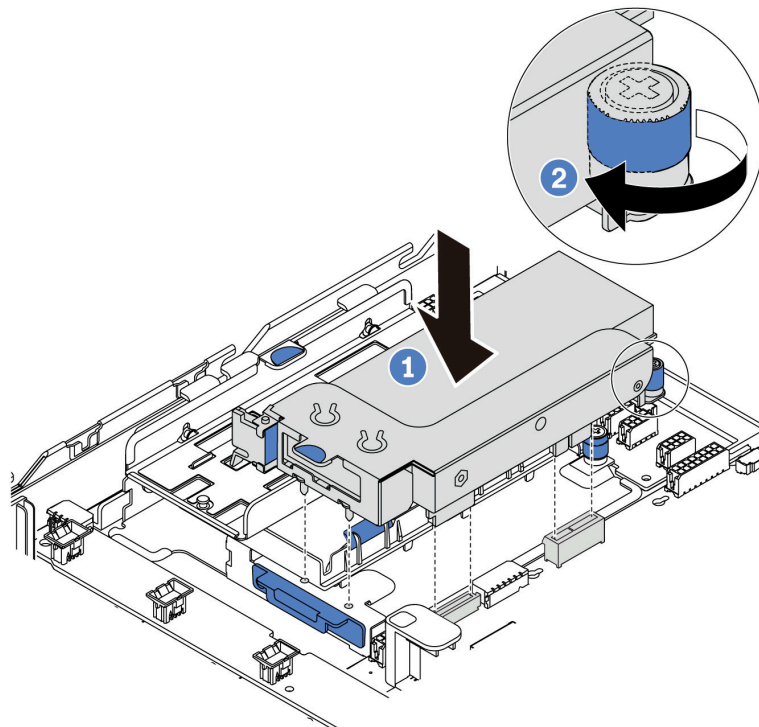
Installation d'un assemblage de cartes mezzanines interne
